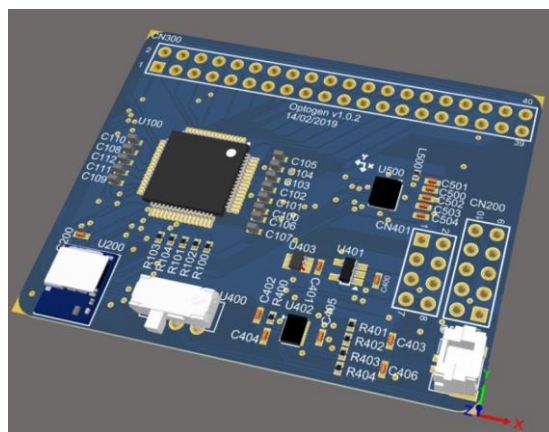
Projeto da PCB Optobrain Interface v1.0
